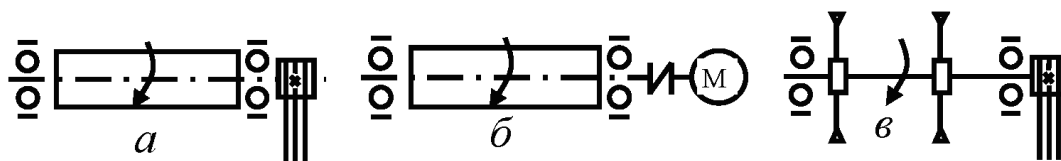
Робочі вали: а, б — ножові вали; в — пильний вал
